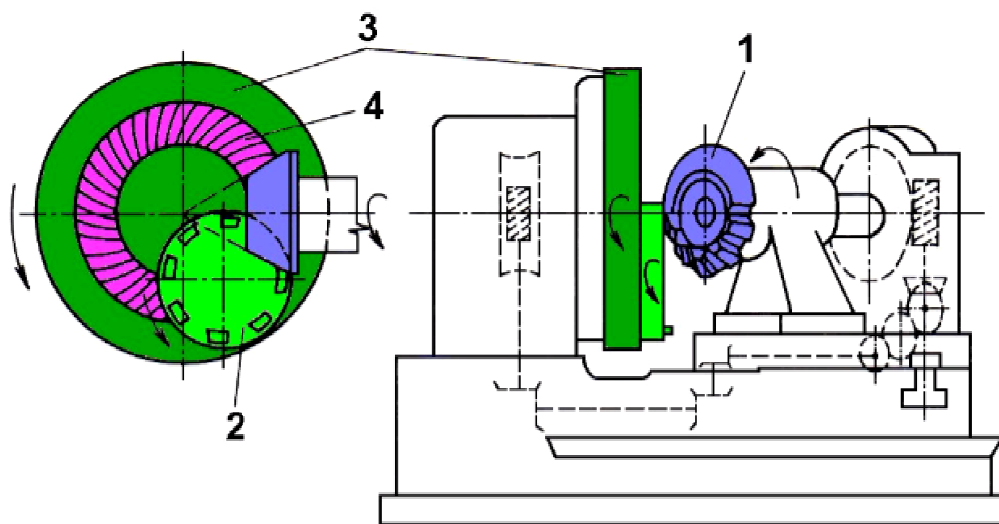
Frézování kuželového ozubení tvarovou kotoučovou frézou [29]
